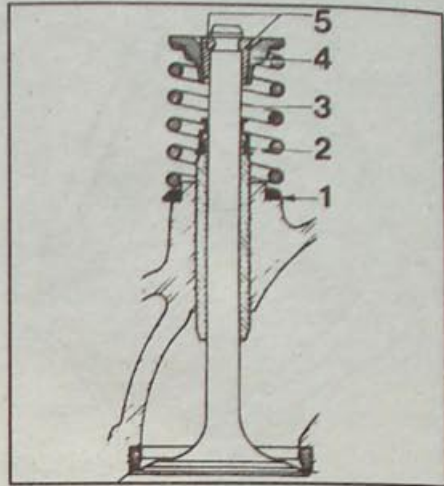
Детали клапана, установленного в головку блока цилиндров:
